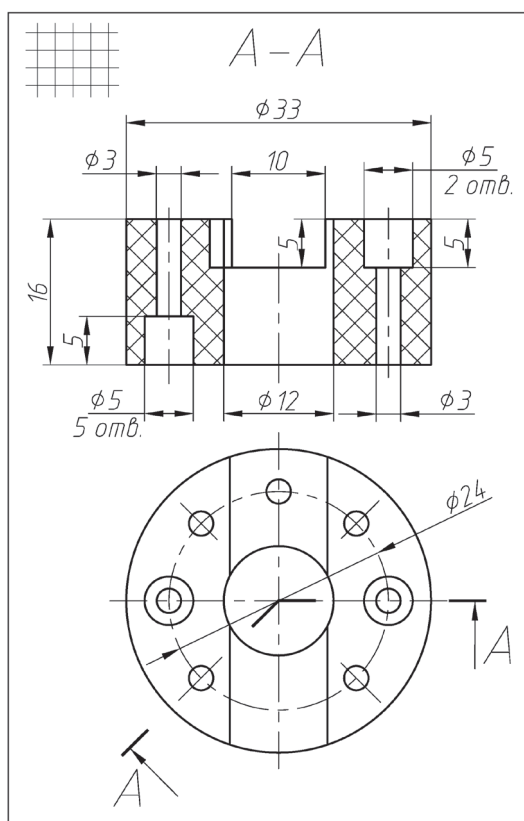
Эскиз детали «Корпус» с натурального образца
